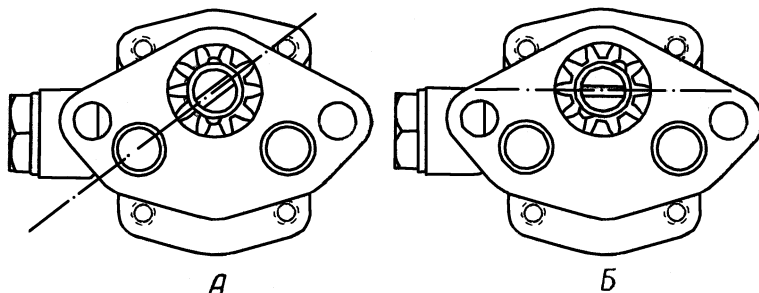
Положение прорези вала масляного насоса (вид на вал сверху):
